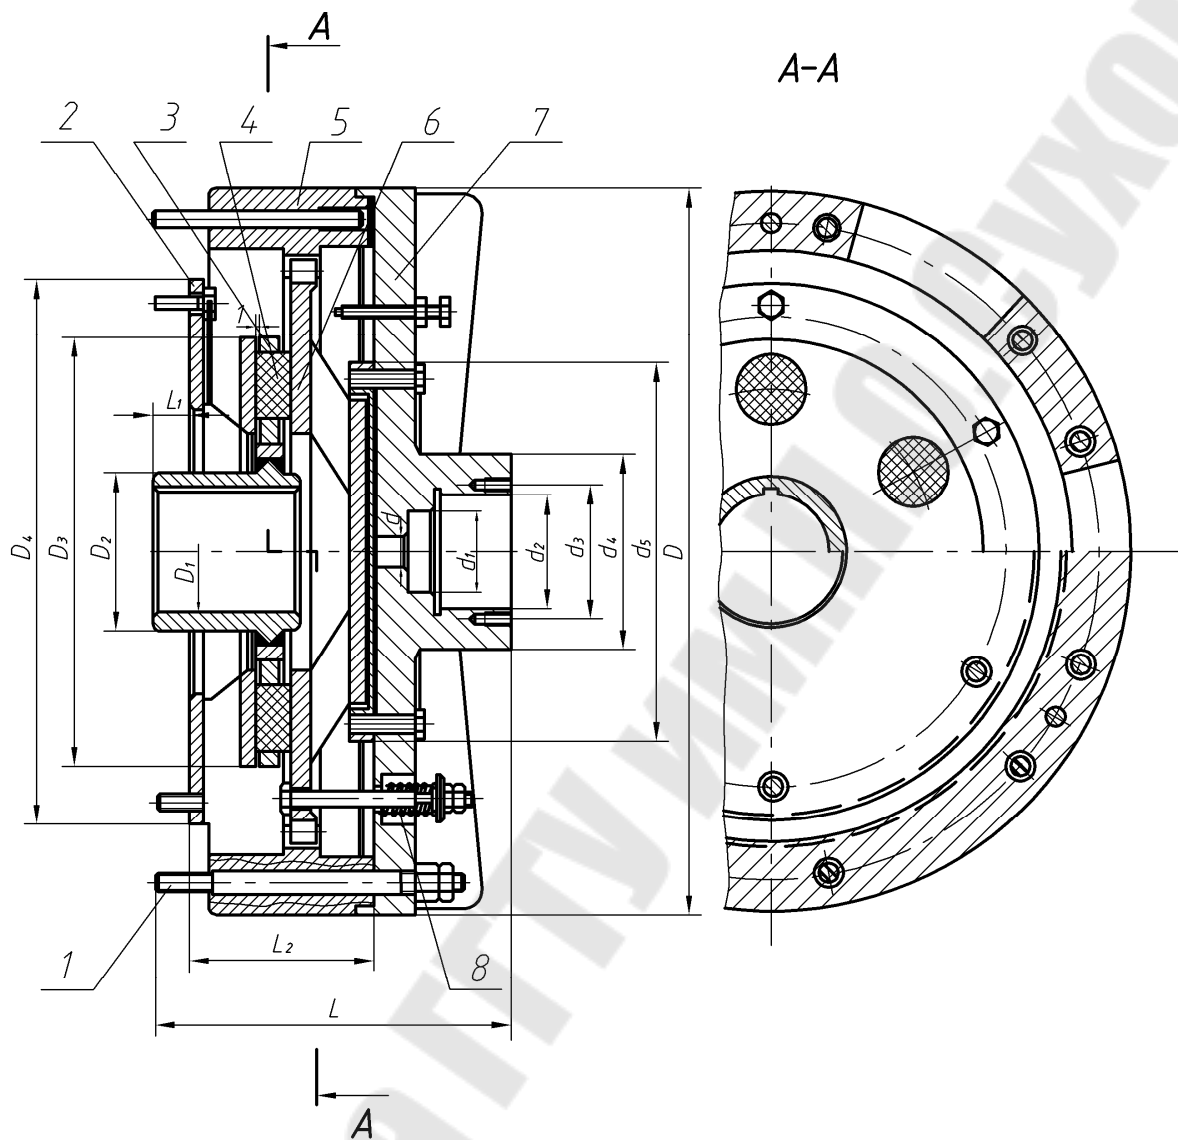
Габаритные и присоединительные размеры пневматических одноопорных муфт
